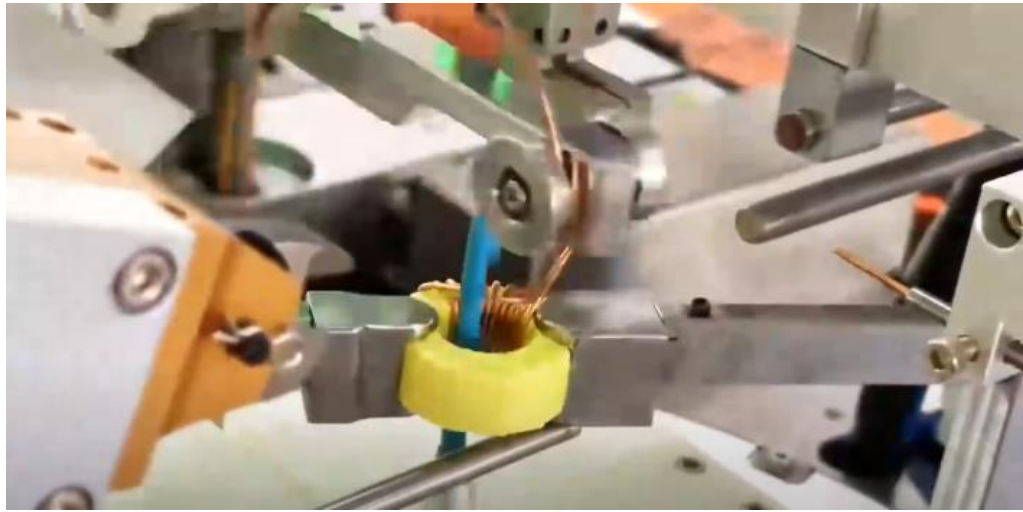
Намотувальний верстат гачкового типу [2]
